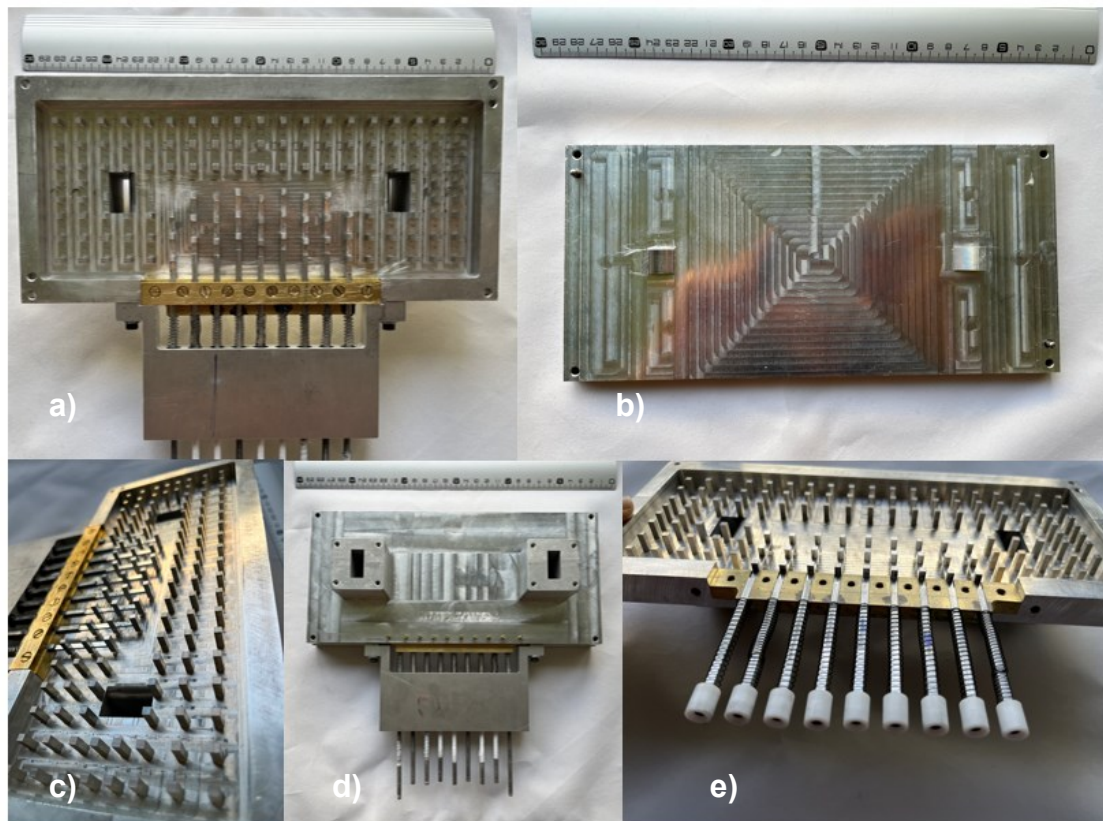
prototype du filtre accordable PF. V1.3, a) vue intérieure du corps principal, b) vue de dessus de la plaque inférieure, c) vue latérale du corps principal (tiges DGGW suspendue), d) vue de dessus du corps principal, e) corps principal sans la butée latérale et sans la plaque de guidage
